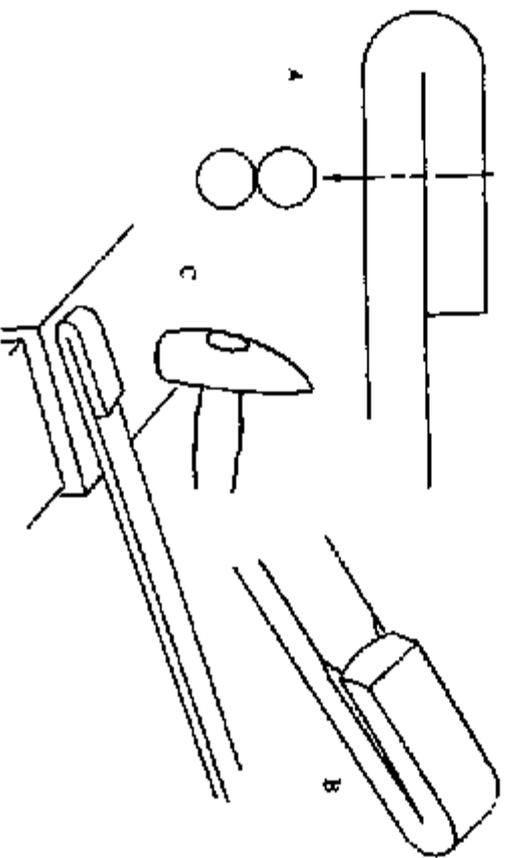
Una soldadura tipo fogot (A) engrosa una barra que ha sido doblada sobre sí misma (B, C).
